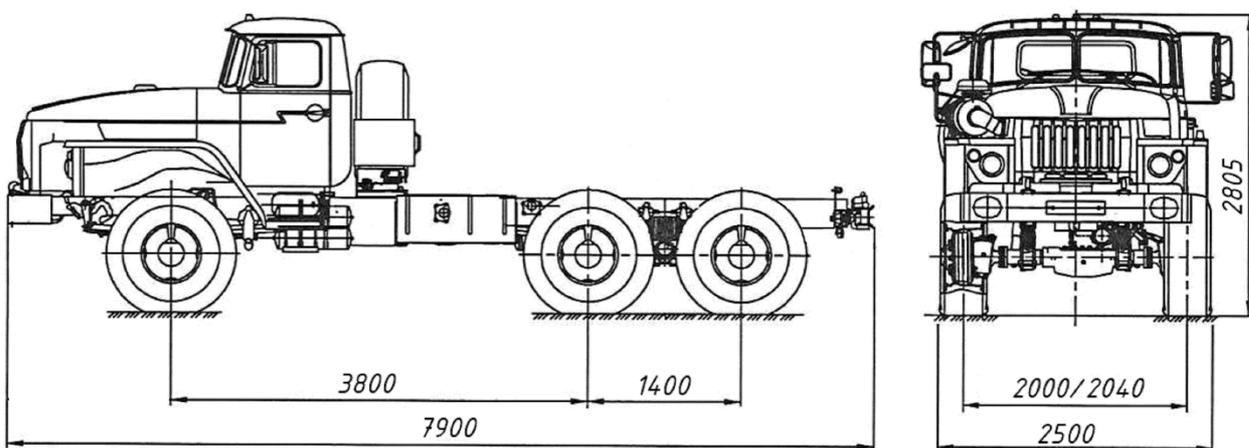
Основные размеры шасси Урал-4320-1151-41
